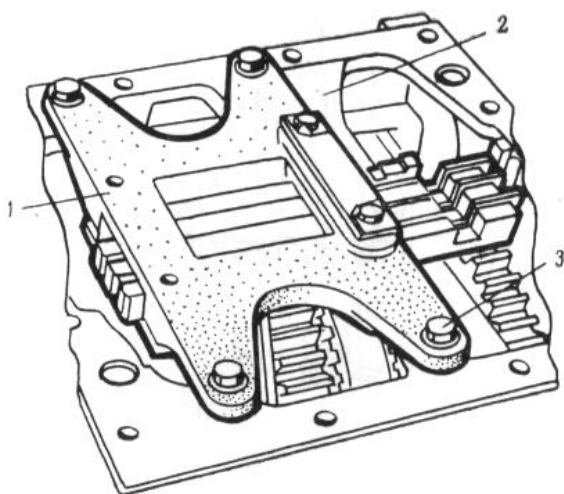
Знімання механізму переключення передач: 1- корпус вилок переключення; 2- корпус коробки передач; 3- болт.
